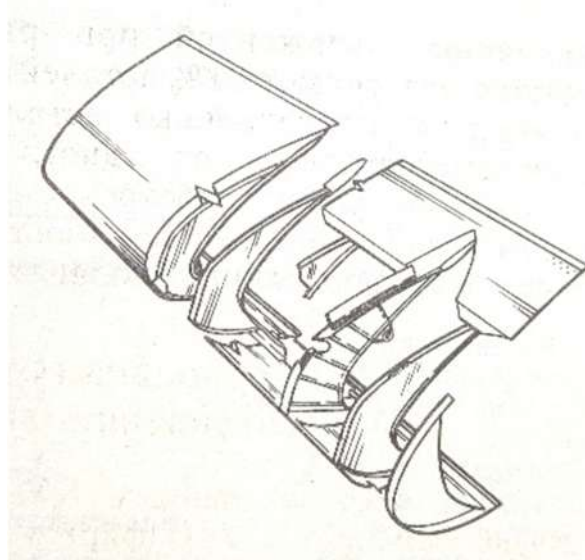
Конструкція передкрилка з боропластика літака С-5А
